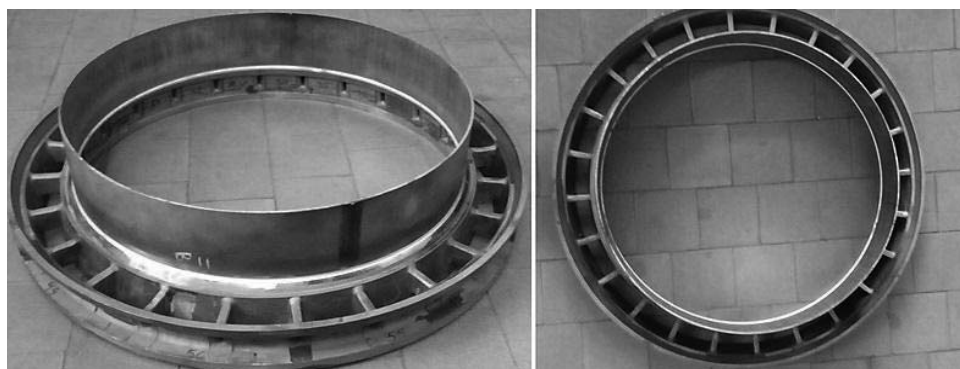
Сварной диффузор конструкции АО «Климов»
